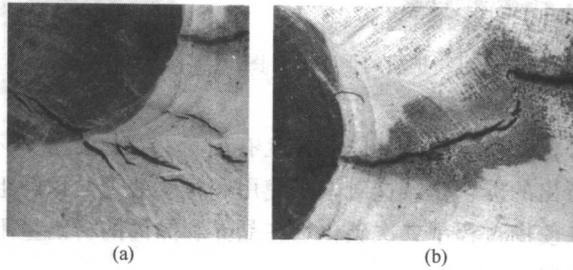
弯头焊缝裂纹的形貌 (12.8×)
